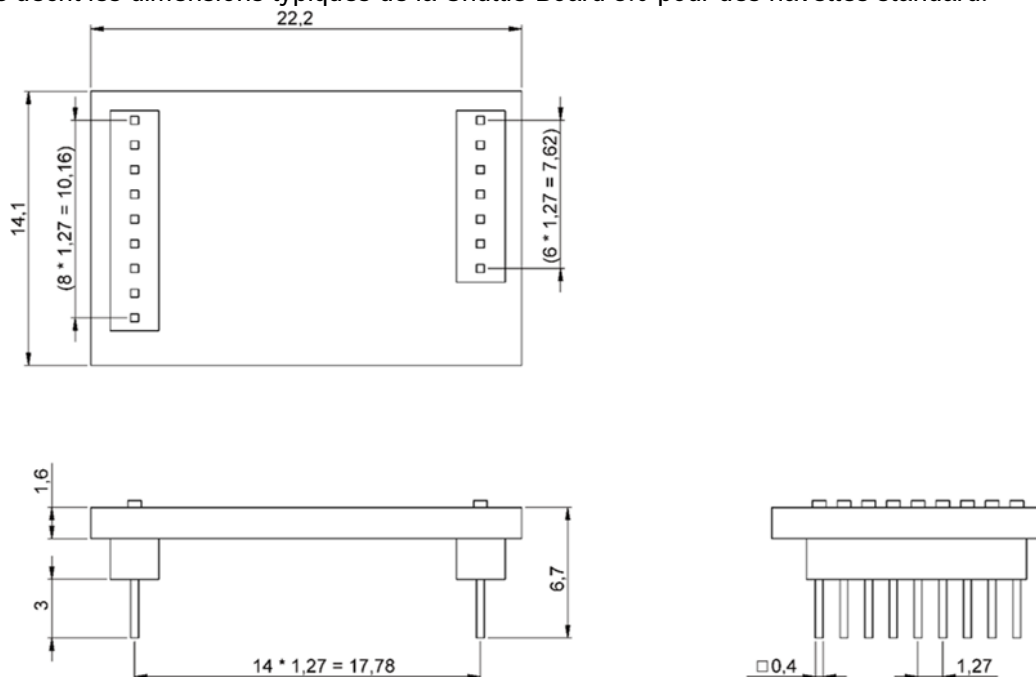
Dimensions de la carte Shuttle Board 3.0 standard
